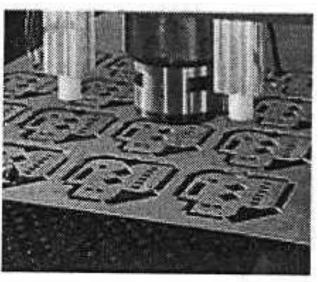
Образцы пробивки на гидравлическом координатно-револьверном пробивочном прессе с ЧПУ
